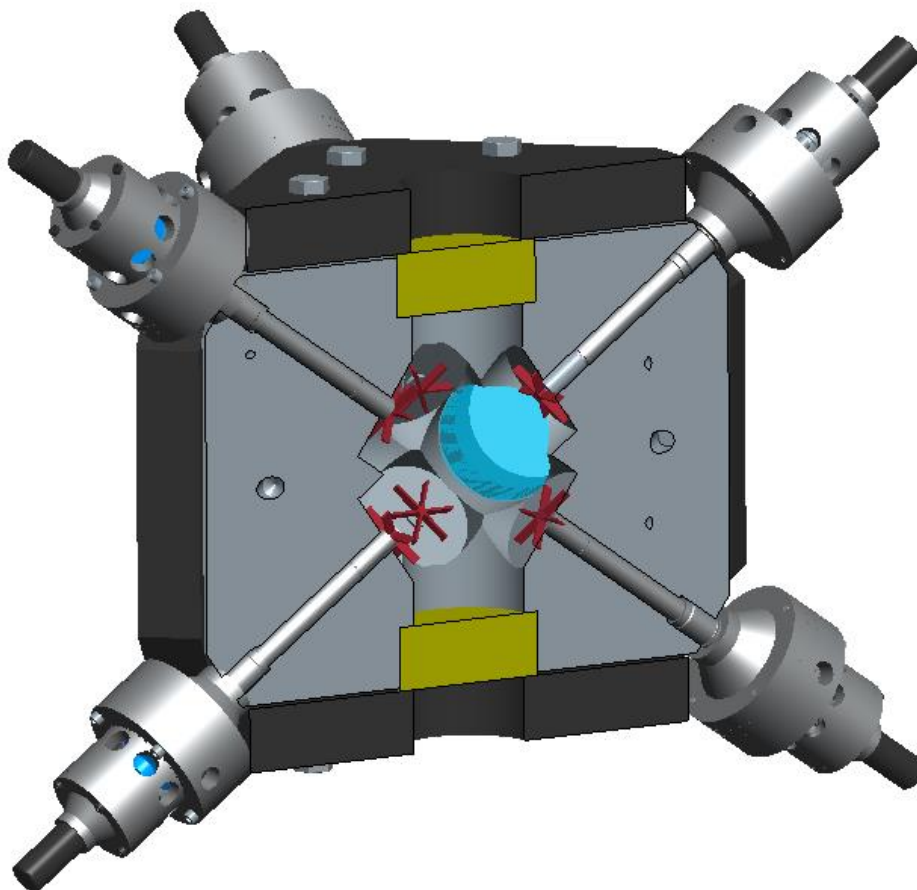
Der Explosionswürfel mit eingebauten Turbulenzerzeugern – Querschnitt
